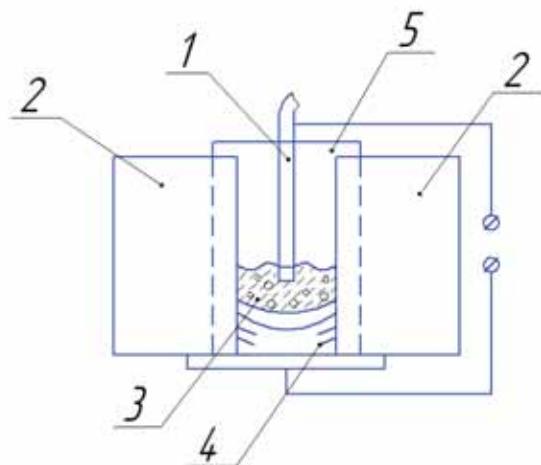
Электрошлаковая сварка: 1 – электрод; 2 – деталь; 3 – шлаковая ванна; 4 – сварной шов; 5 – ползуны-кристиллизаторы
